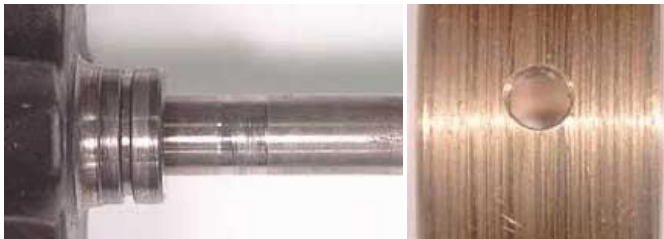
Вид зносу деталей роторного вузла турбокомпресора
